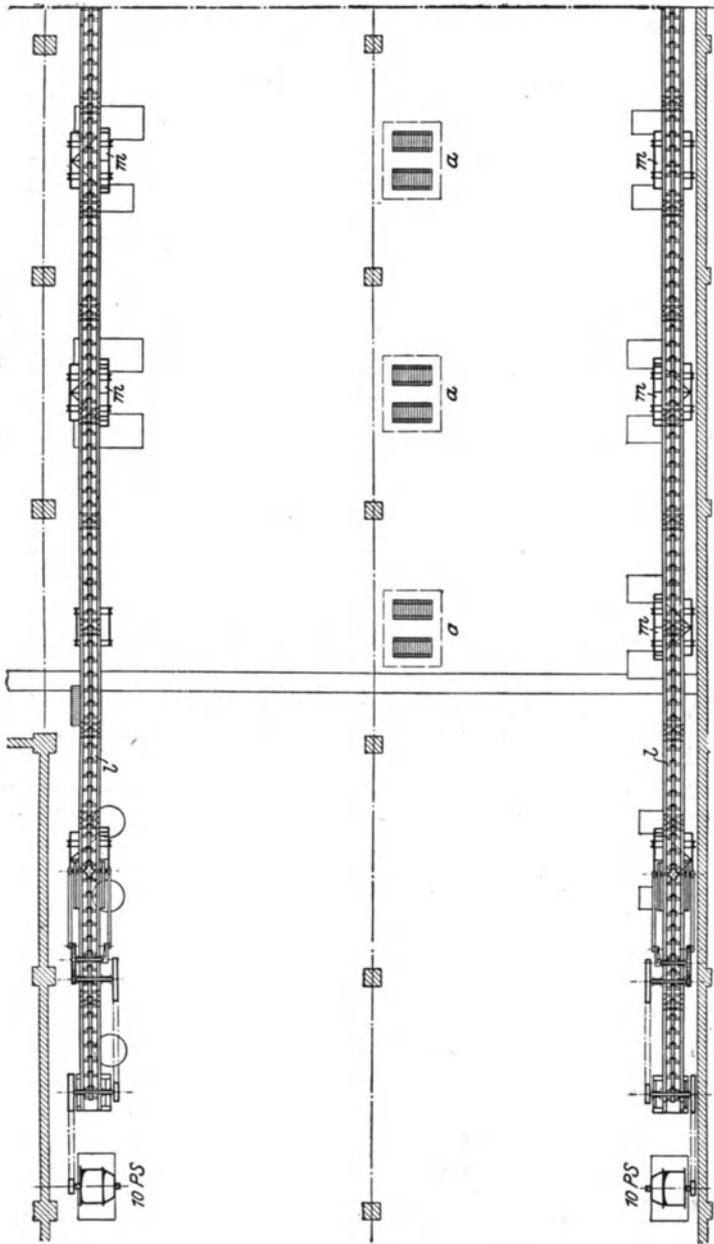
a. Sandaufbereitungs- und Förderanlage. Grundriß des Erdgeschosses.
